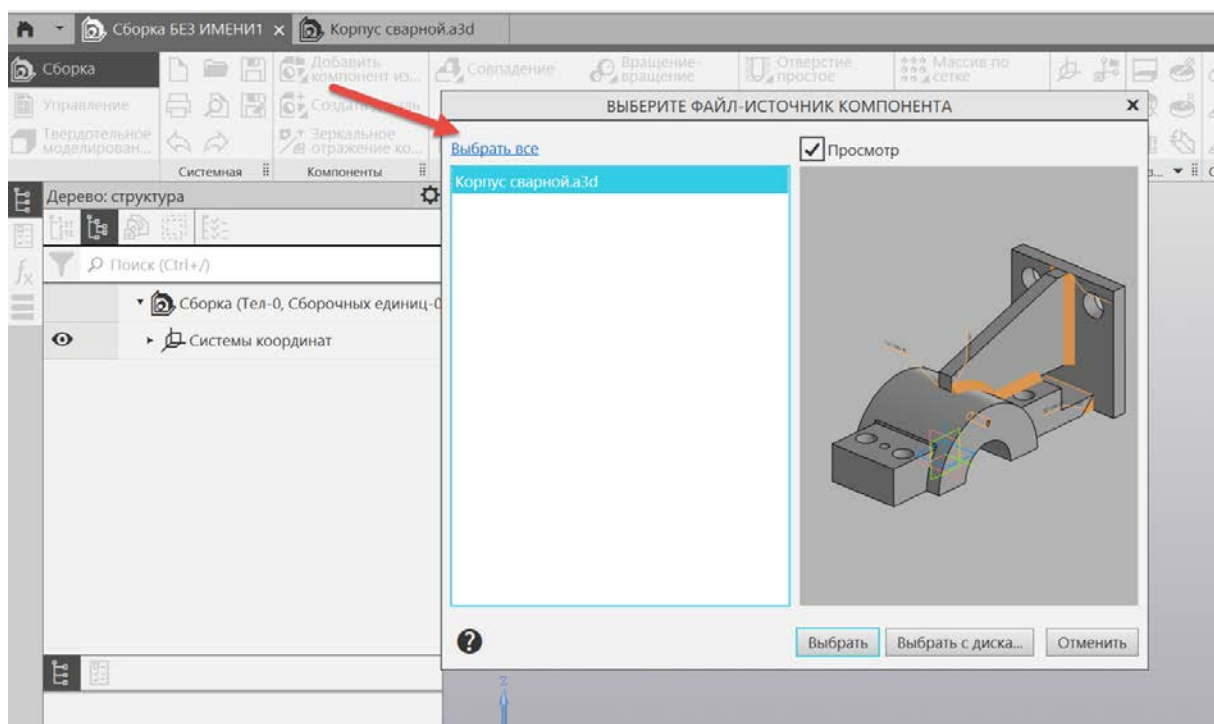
Добавление в сборку корпуса сварного
